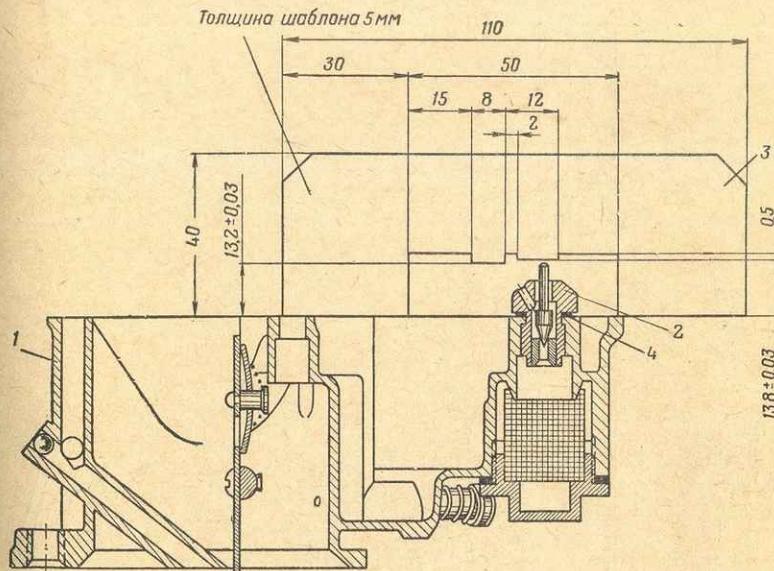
Проверка монтажа игольчатого клапана поплавковой камеры:
